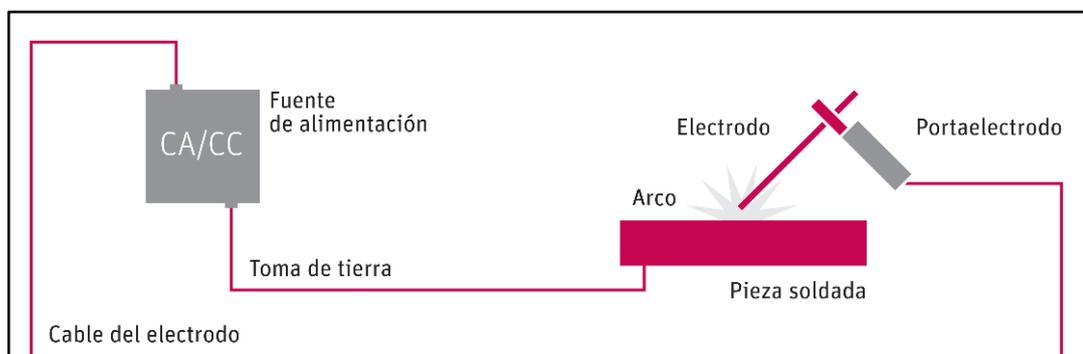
Esquema del proceso de soldadura eléctrica por arco
